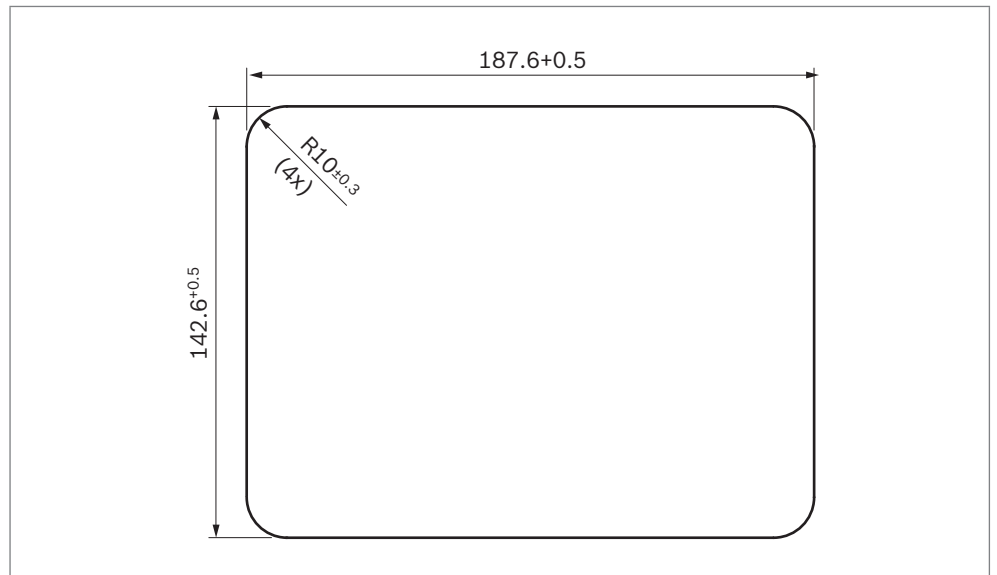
Ausschnitt für Einbau eines DI3 in ein Armaturenbrett
